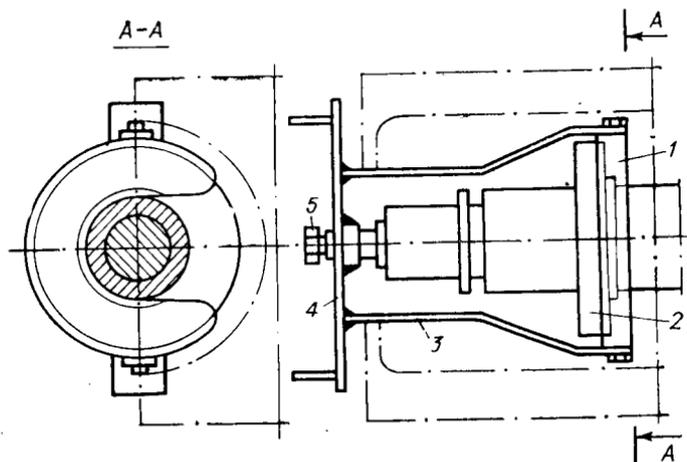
Приспособление для шлифовки упорного диска:
